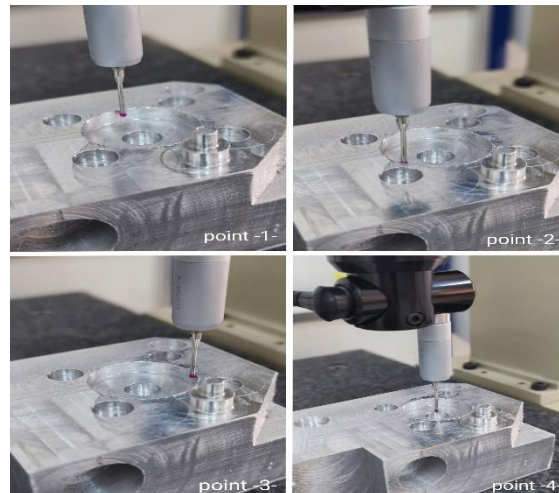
Déterminer la circularité de la pièce à l'aide d'une machine.
